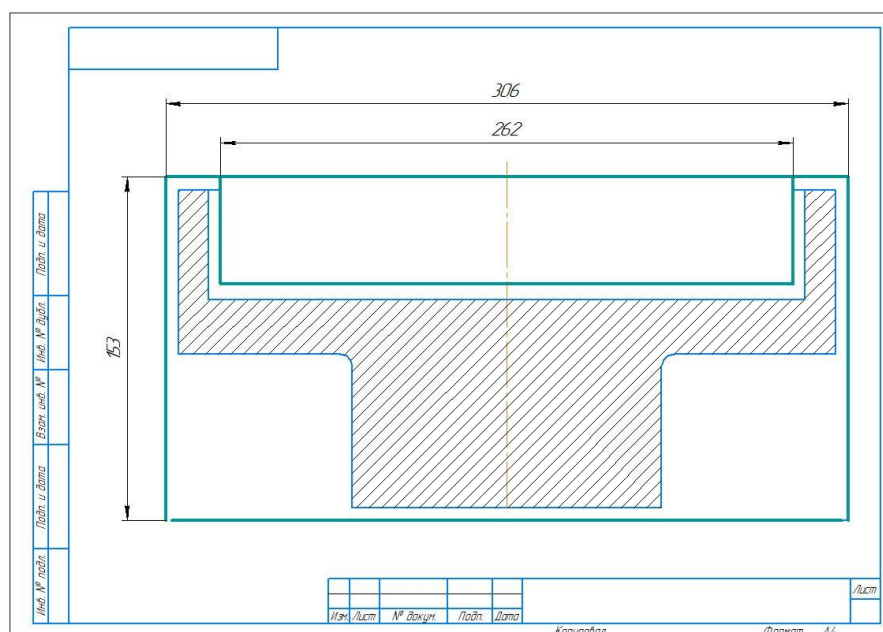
Заготовка деталі "Напівмуфта"
